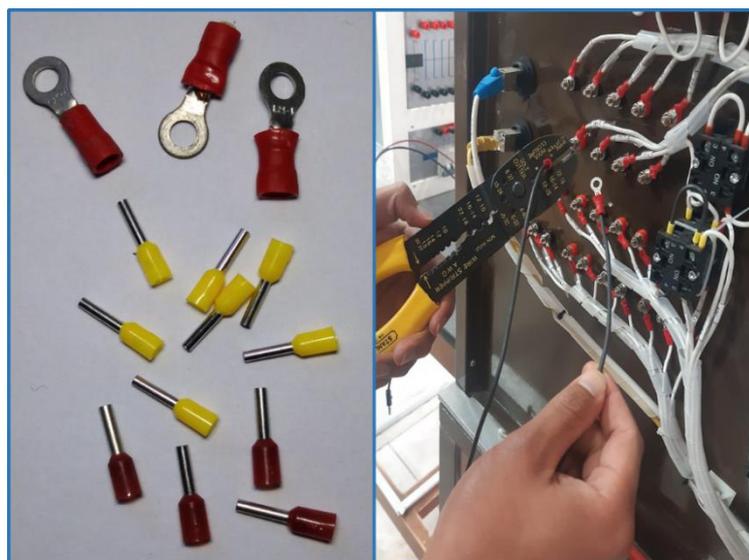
Tipos de terminales usados y su colocación en el cableado.
